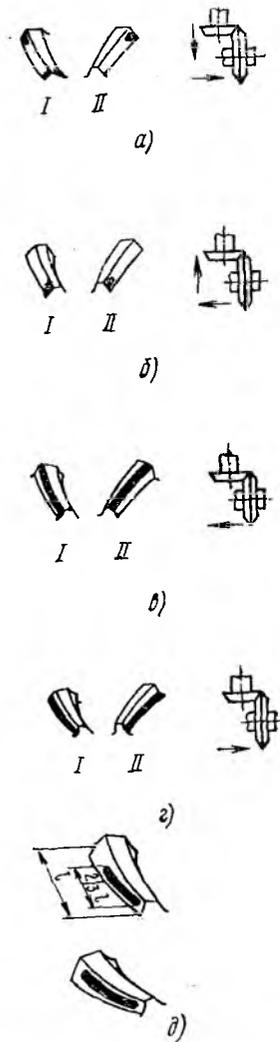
Регулирование зубчатого зацепления косо-зубой пары главной передачи:
